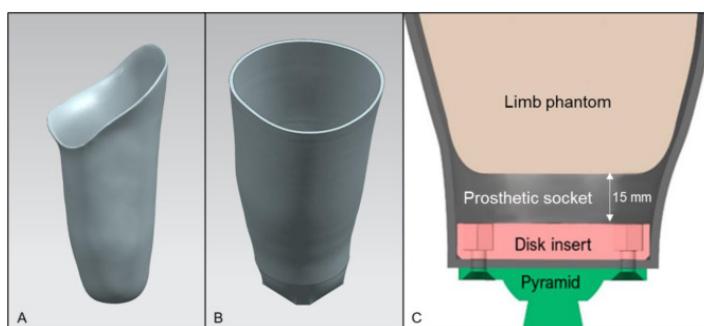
(A) Diseño original del socket. (B) Diseño del socket utilizado para pruebas mecánicas. (C) Detalles del mecanismo de fijación del socket.
